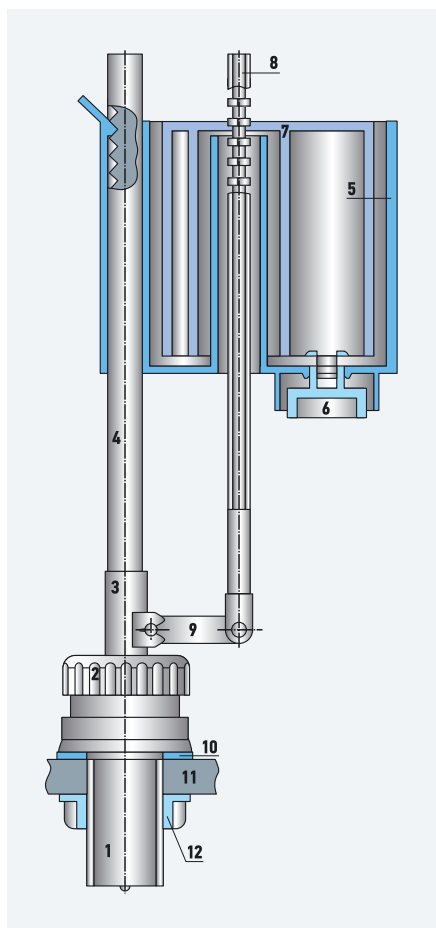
Конструктивная схема наполнительной арматуры с сервоуправлением с нижней подводкой ЗАО «Уклад» (1 — корпус арматуры; 2 — накидная гайка; 3 — втулка; 4 — стойка; 5 — емкость для поплавка; 6 — обратный клапан емкости; 7 — поплавок; 8 — тяга; 9 — рычаг; 10 — уплотнительная прокладка; 11 — дно смывного бачка; 12 — крепежная гайка)
